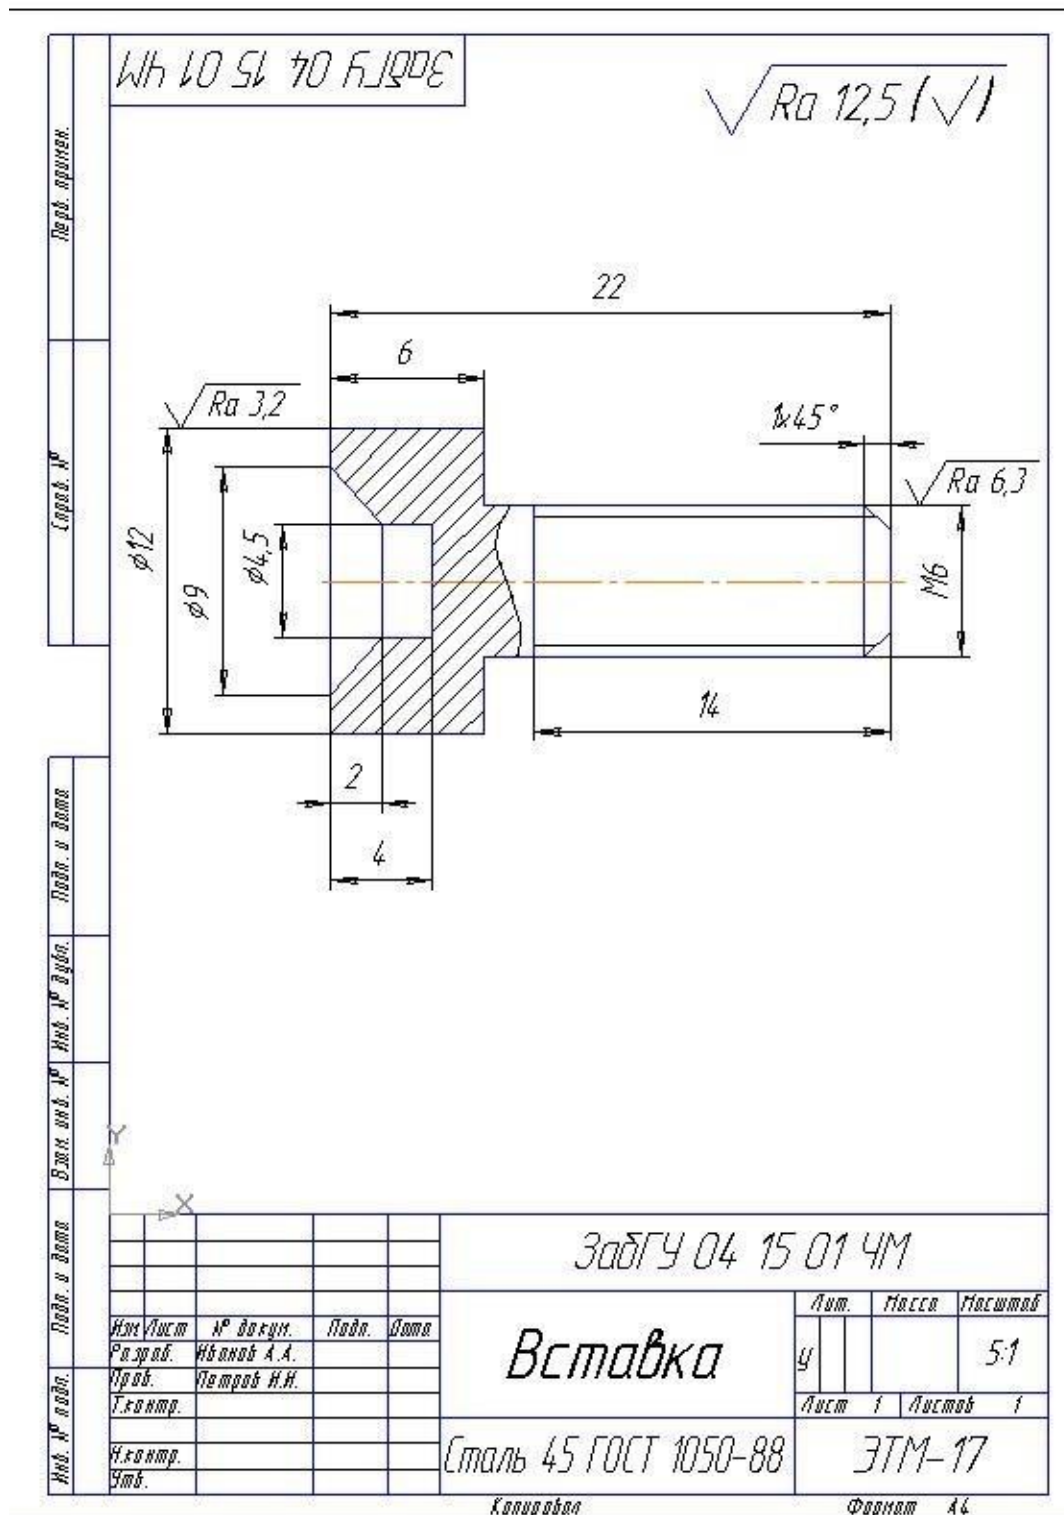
Образец выполнения задания «Рабочий чертёж детали»
